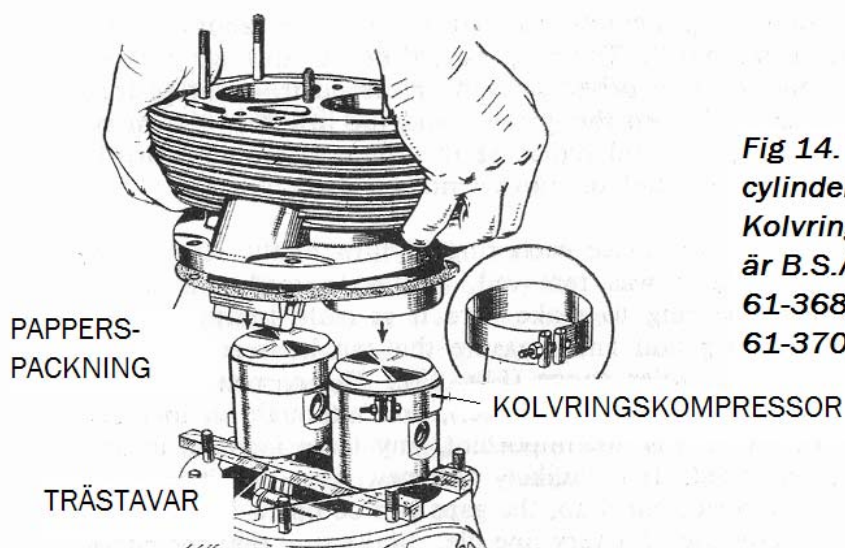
Montering av cylinderblocket. Kolvringskompressorerna är B.S.A. serviceverktyg: 61-3682 (500 cc motor), 61-3707 (650 cc motor).
